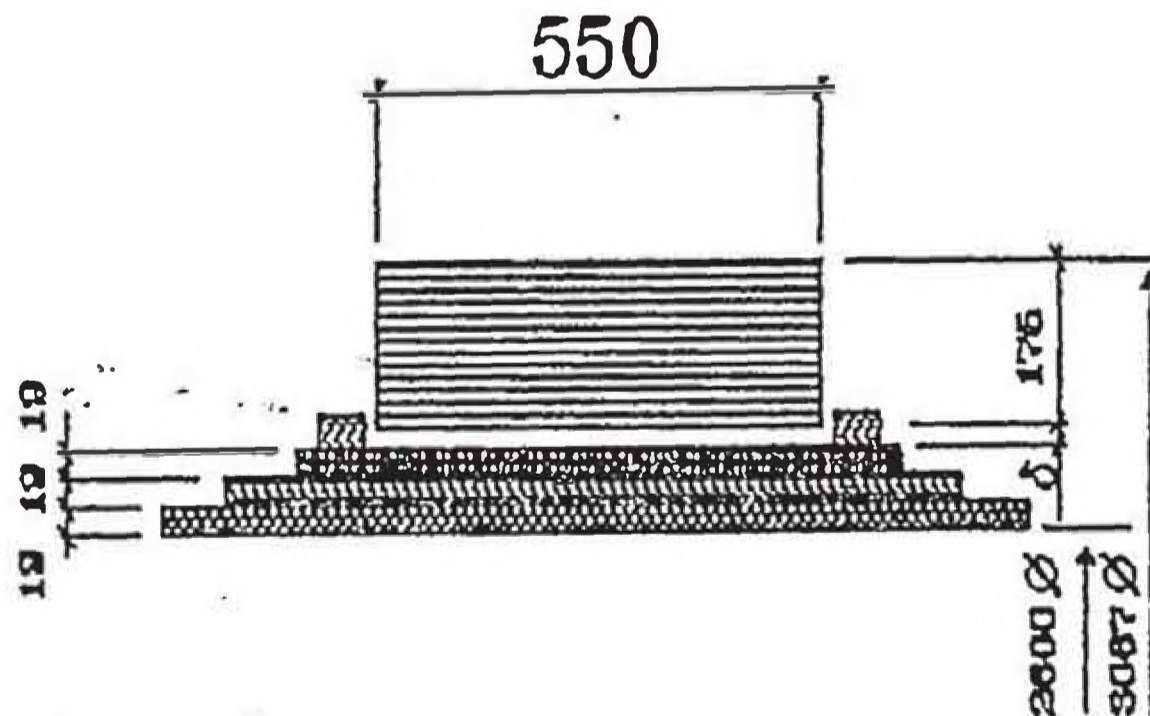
DISPOSICION TIPICA DE UNA LLANTA DE RODADURA ENSAMBLADO EN LA VIROLA
